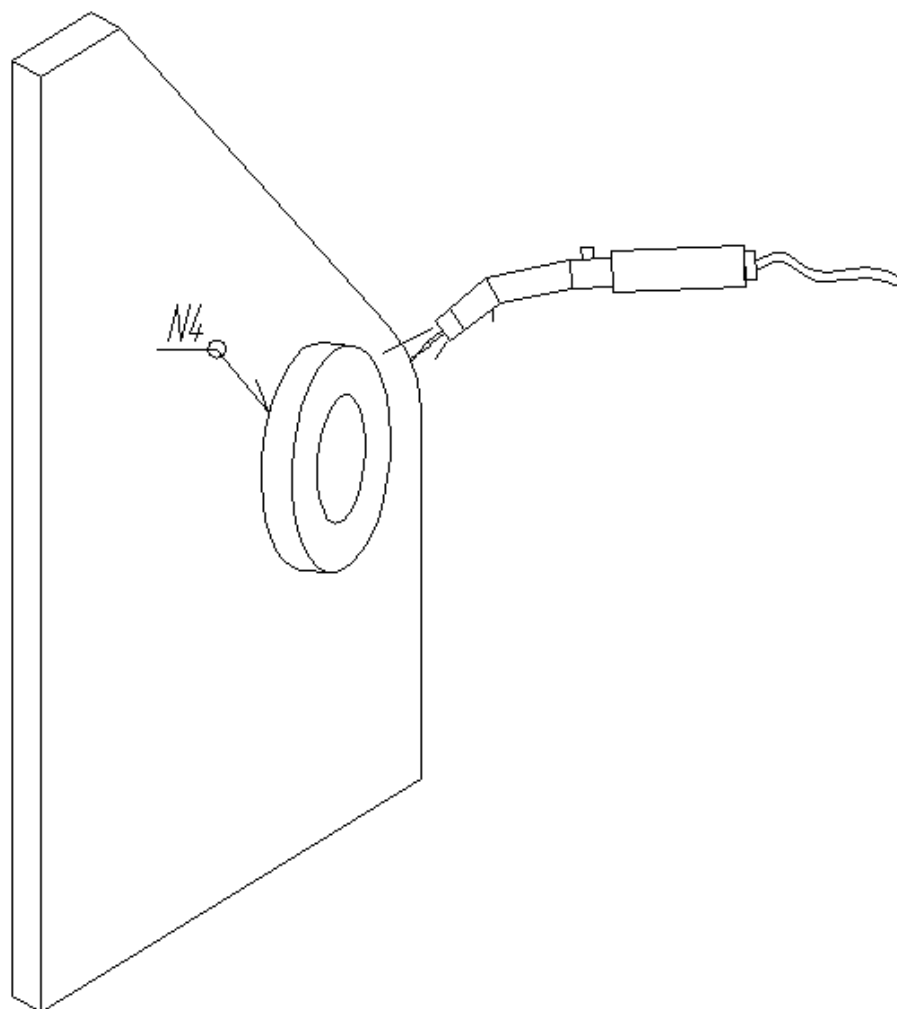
Сварка кольцевого шва втулки и кронштейна
